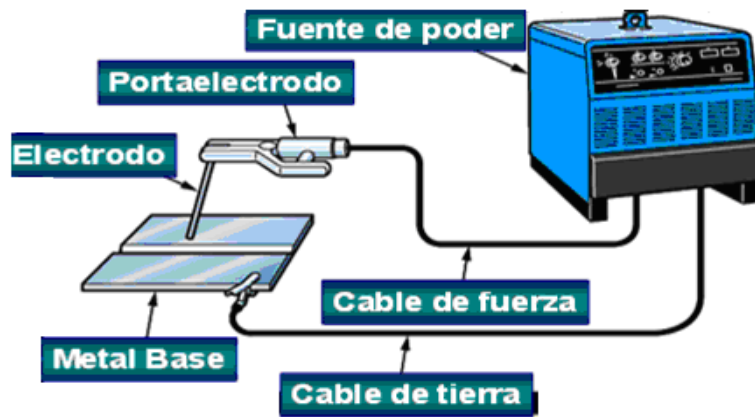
Circuito de soldadura para arco eléctrico con electrodo revestido
